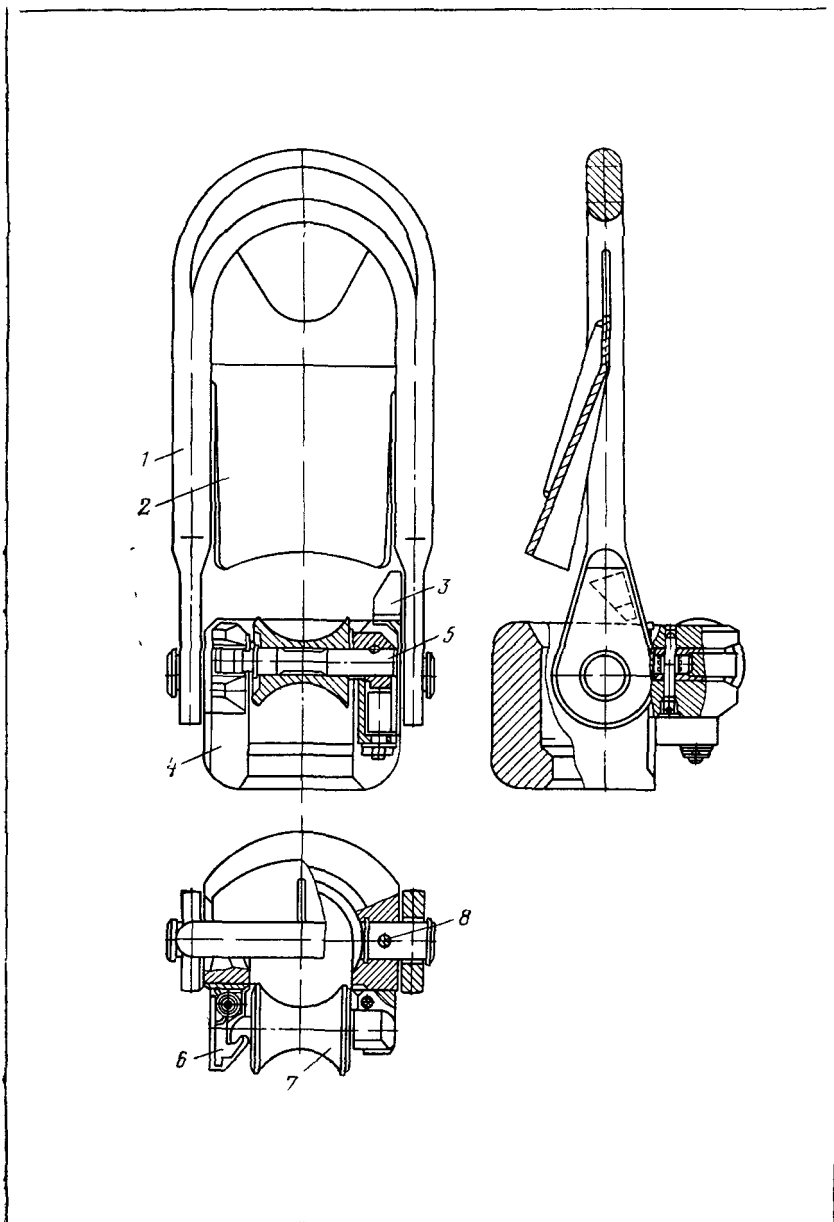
Полуавтоматический элеватор МЗ-50-80:
